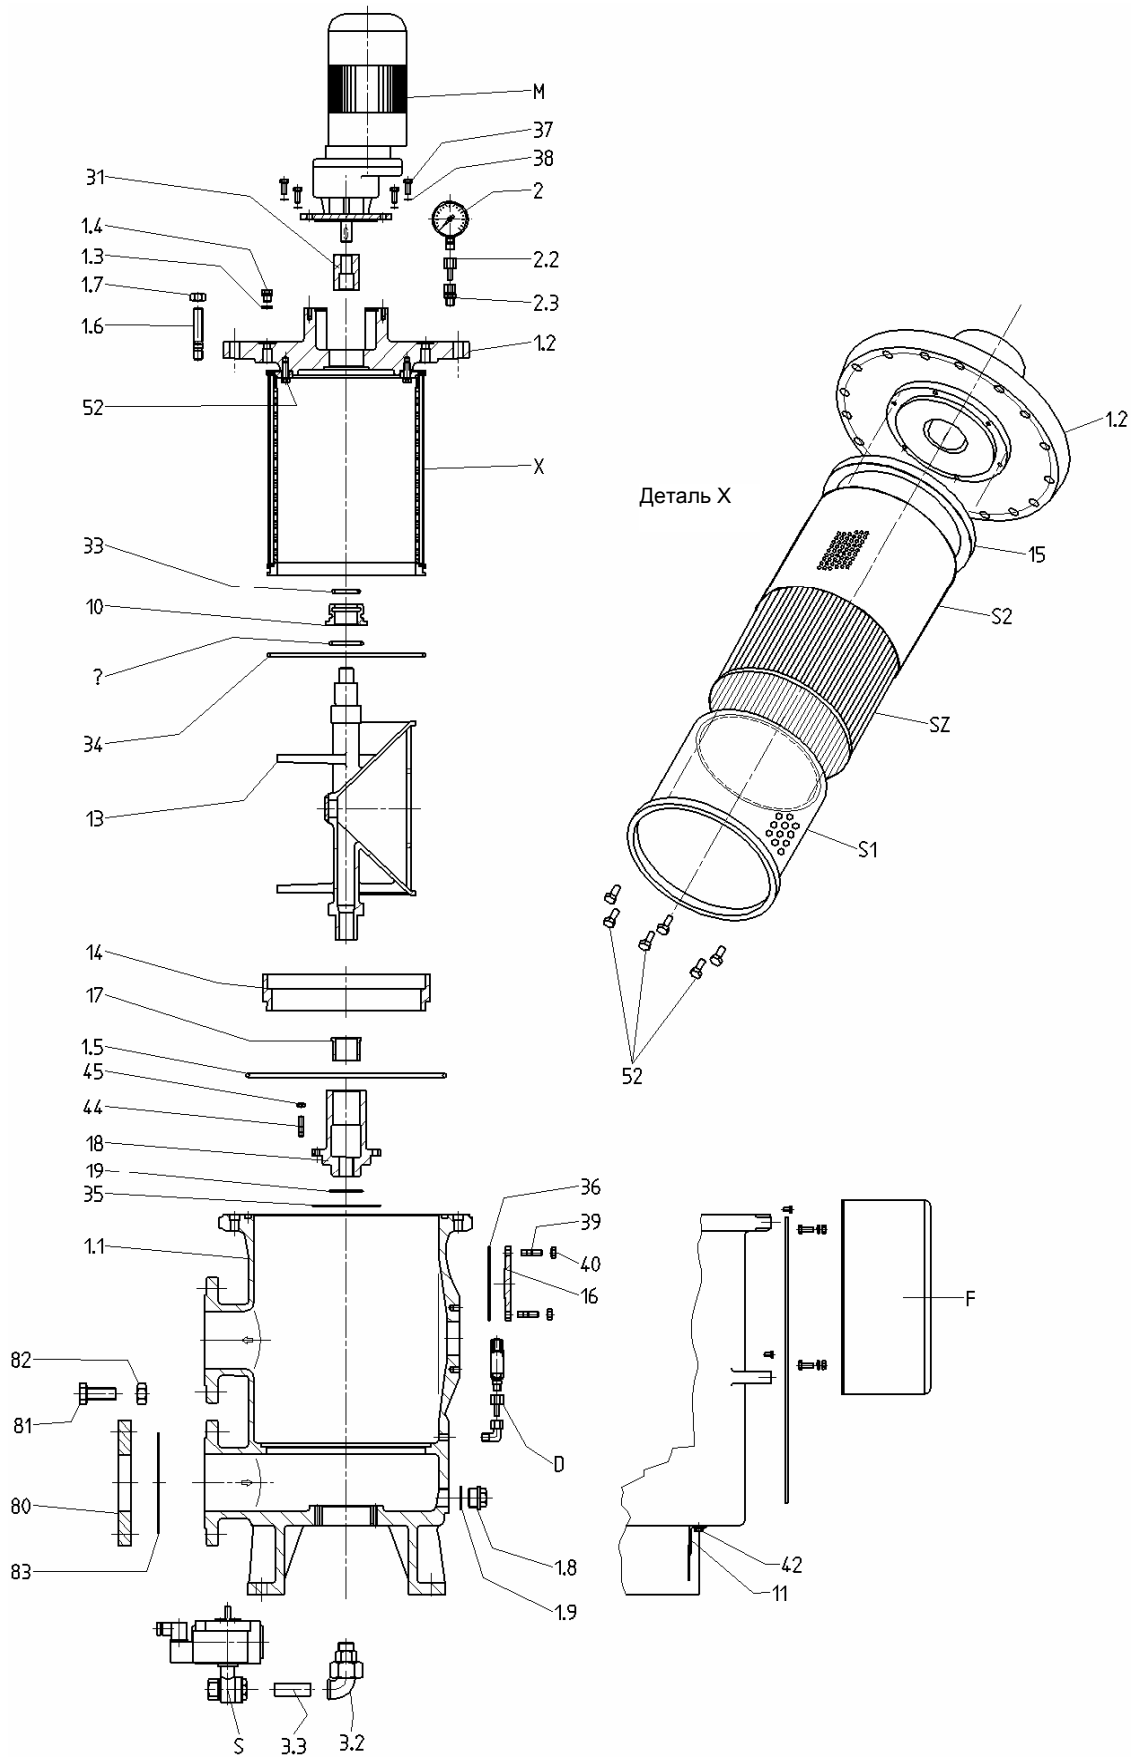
Чертёж деталей R5-8 DN65 - DN200
